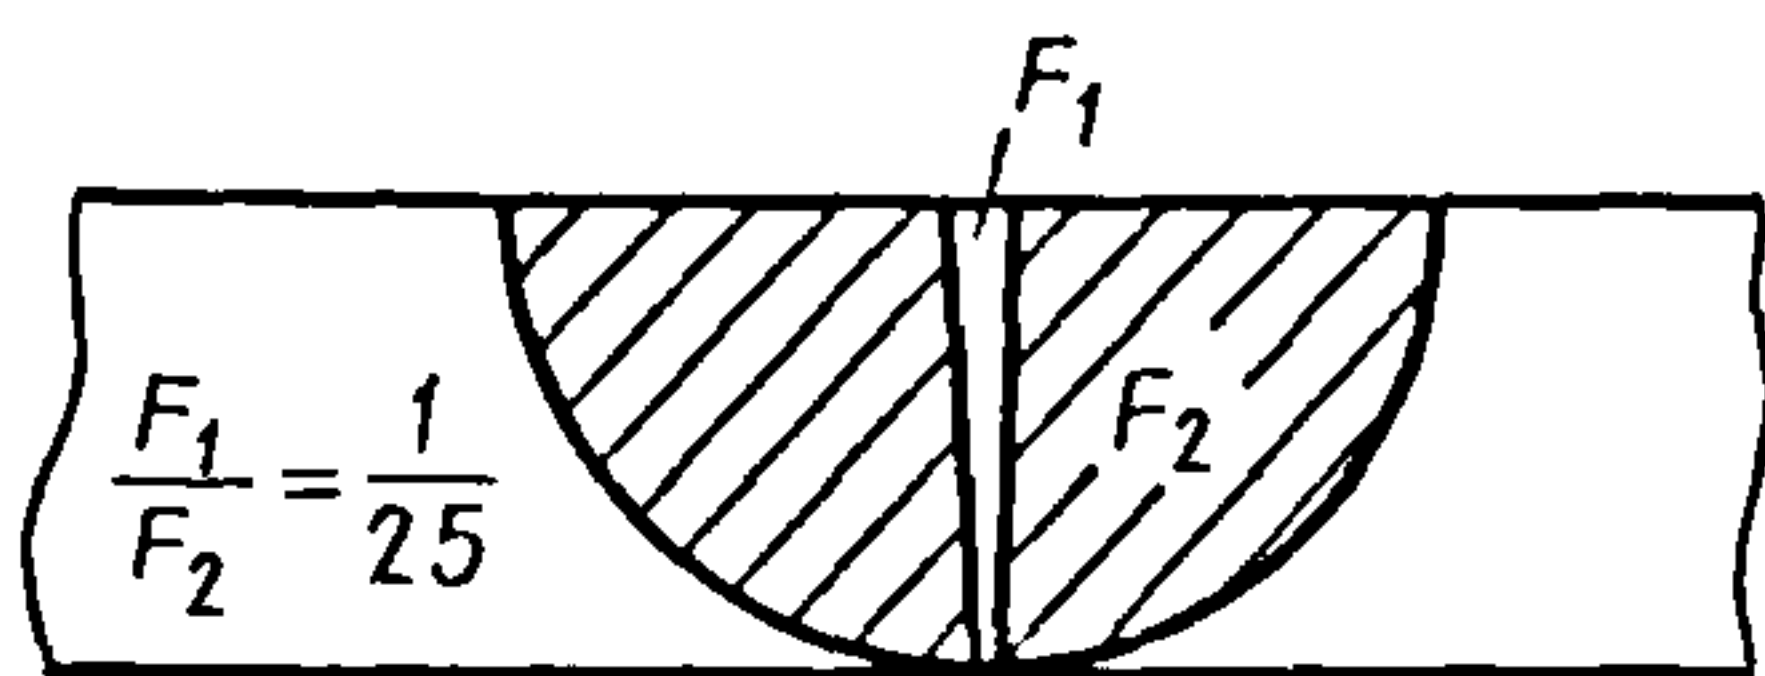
Схема расплавления материала при сварке:
